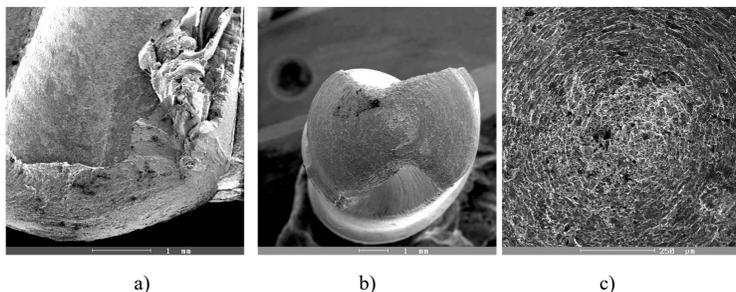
Сгоревшее спиральное сверло а-общий вид, б-вид сверху, в-деталь конструкции
